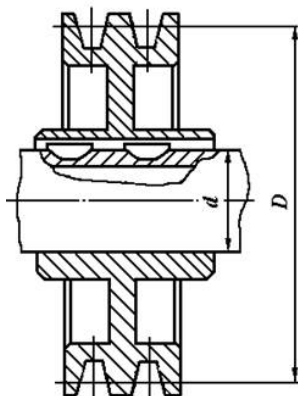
Сегментные шпонки для соединения вала с шкивом
